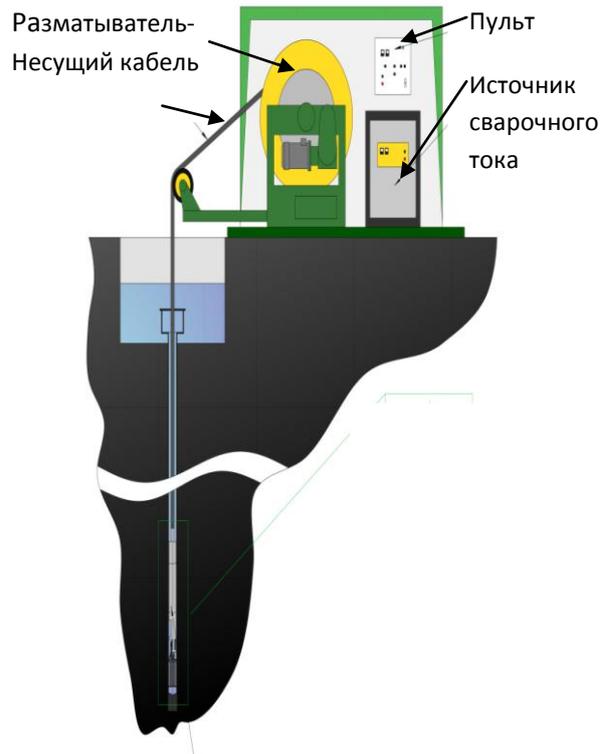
Полный комплекс автомата для глубоководной подводной сварки мокрым способом
